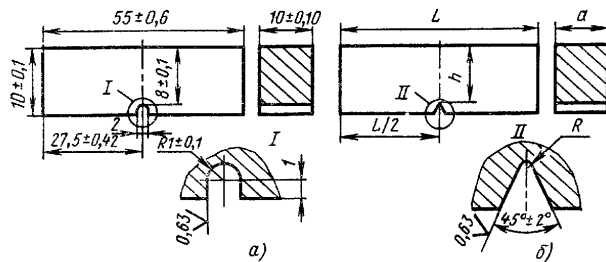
Образцы для испытаний металла шва, околошовной зоны (в различных участках) и наплавленного металла на ударный изгиб
